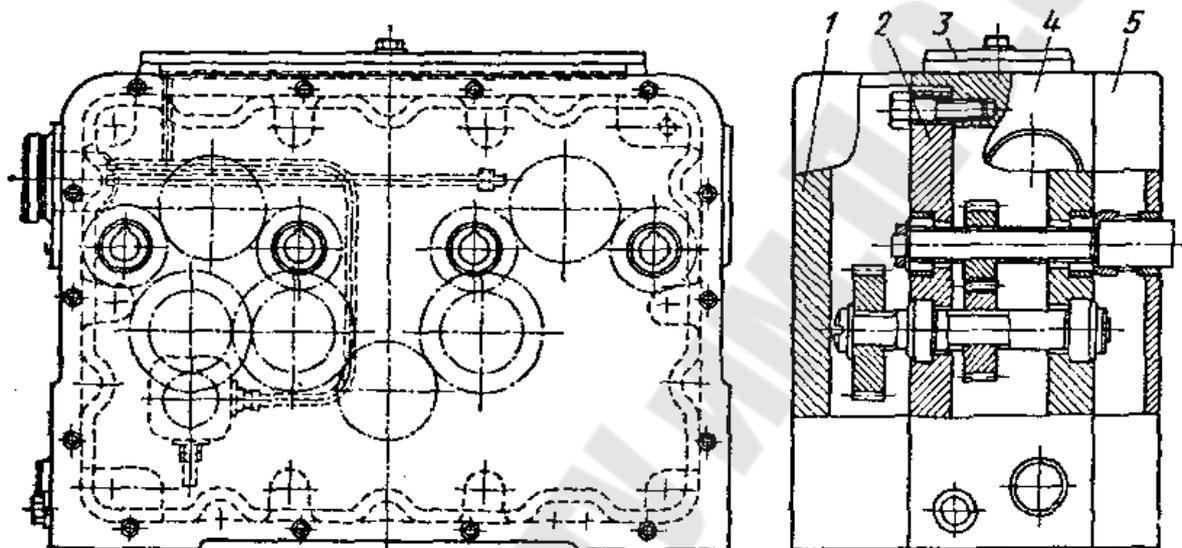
Шпиндельная коробка агрегатного станка
